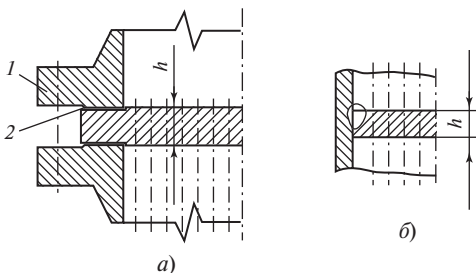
Крепление трубной доски к корпусу аппарата:
